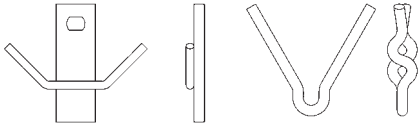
Zweiteiliges Ankerset. Der Schaft (links im Bild) wird mit dem Stahlmantel verschweißt. Nach der Installation der Isolierschicht wird die Ankerspitze (rechts im Bild) in den Schaft eingefädelt /6/.
